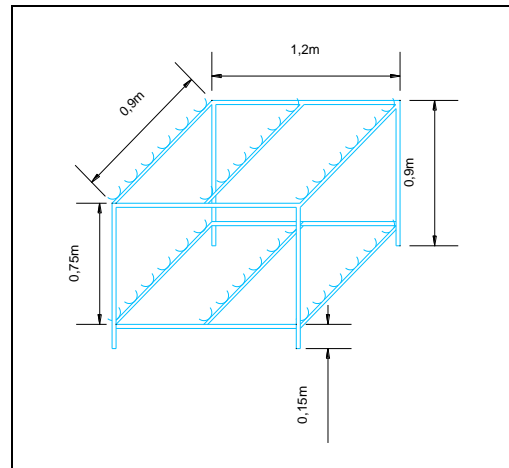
Dimensiones de la estructura metálica para sistema hidropónico.
